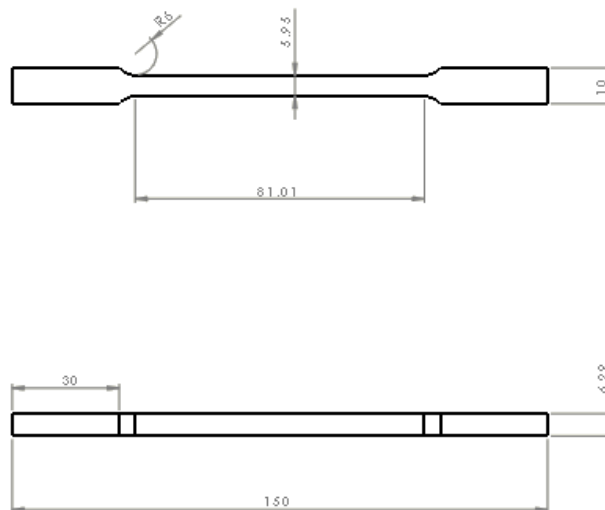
Dimensiones de probeta acotado en mm (probeta 3) [20].
